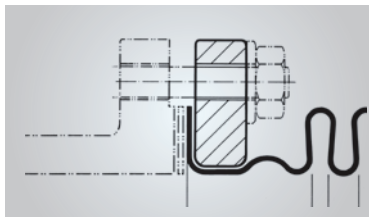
Formschlüssige Verbindung Balg / Bördelflansch
